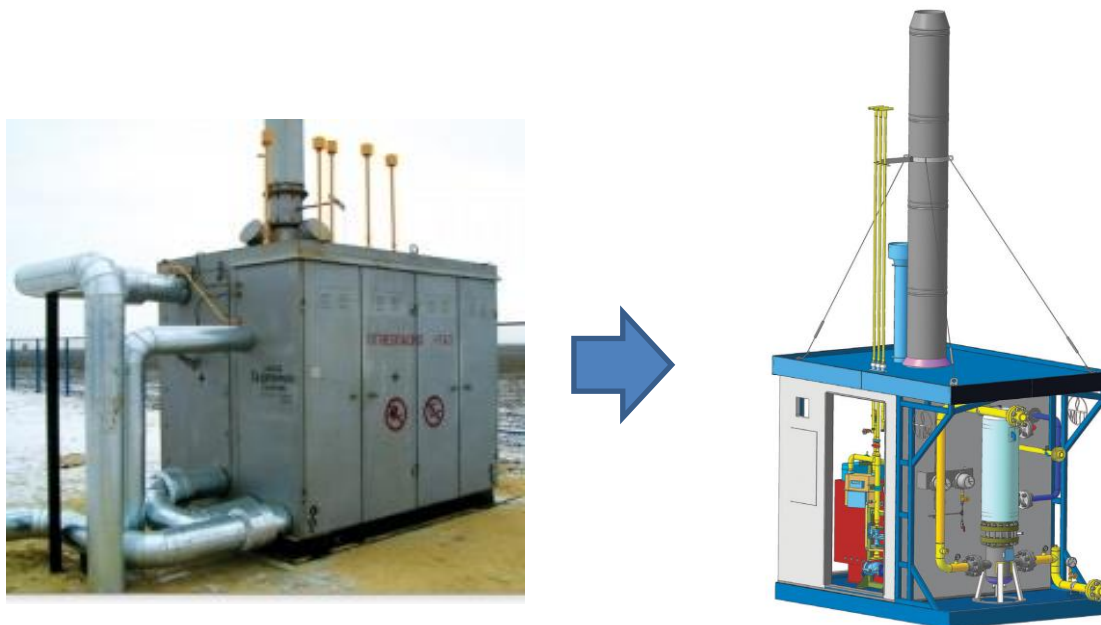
Подогреватель прямого нагрева ПГА-200 и предназначенный для его замены перспективный подогреватель модульной конструкции [2]
